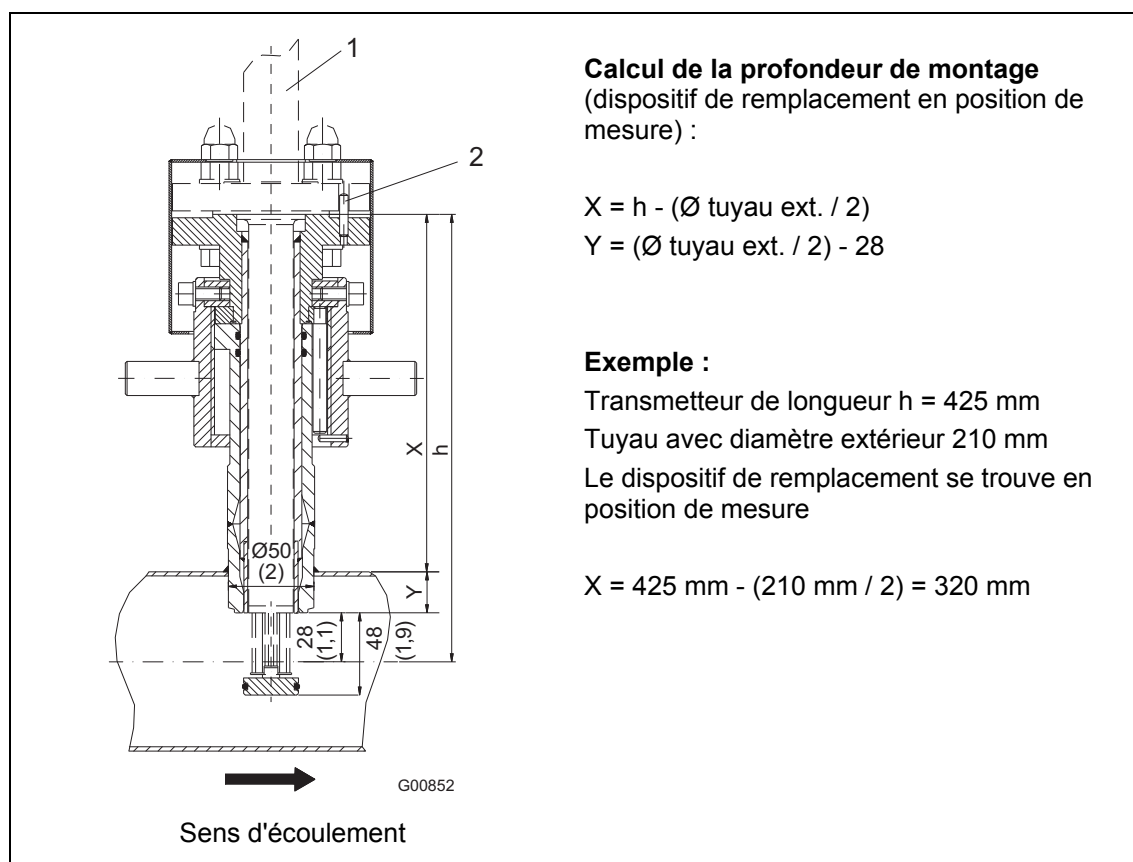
Dimensions en mm (inch). de remplacement intégré en position de mesure
